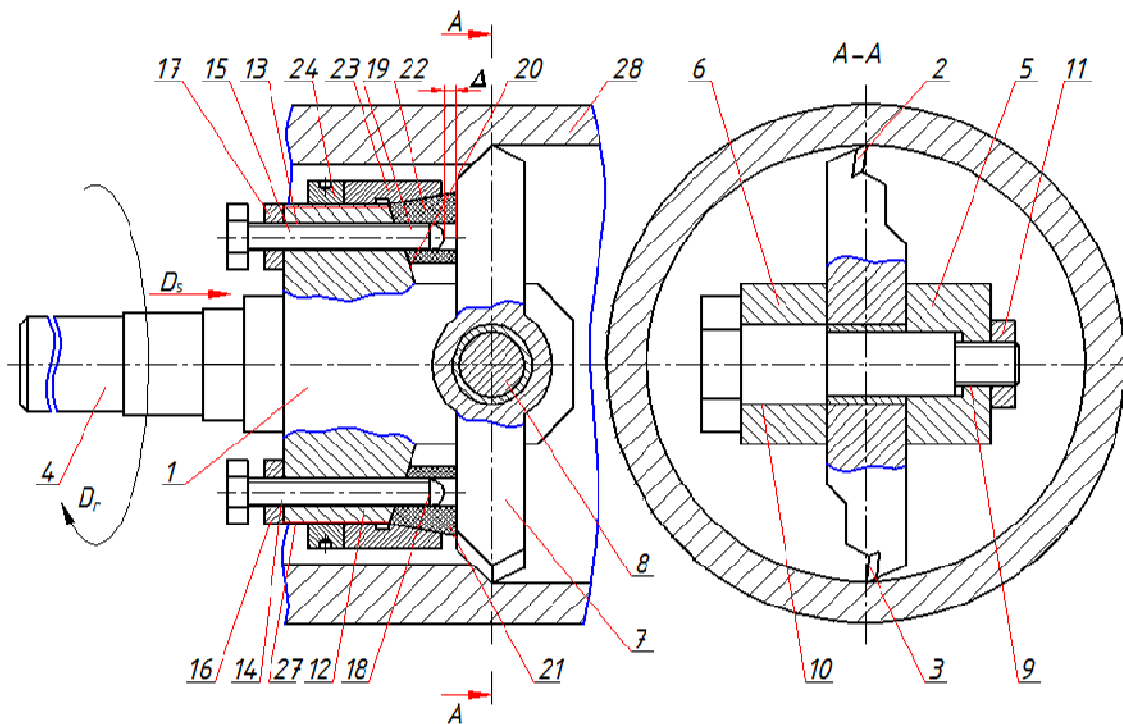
Схема адаптивної дворізевої розточувальної головки
